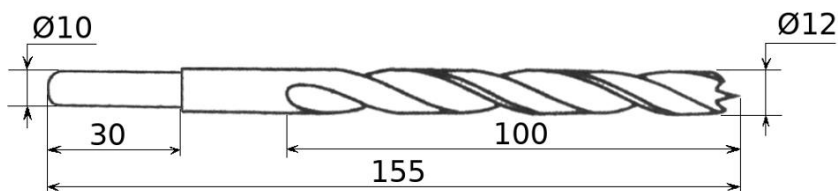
Эскиз детали «Сверло», материал – сталь 9ХС.
